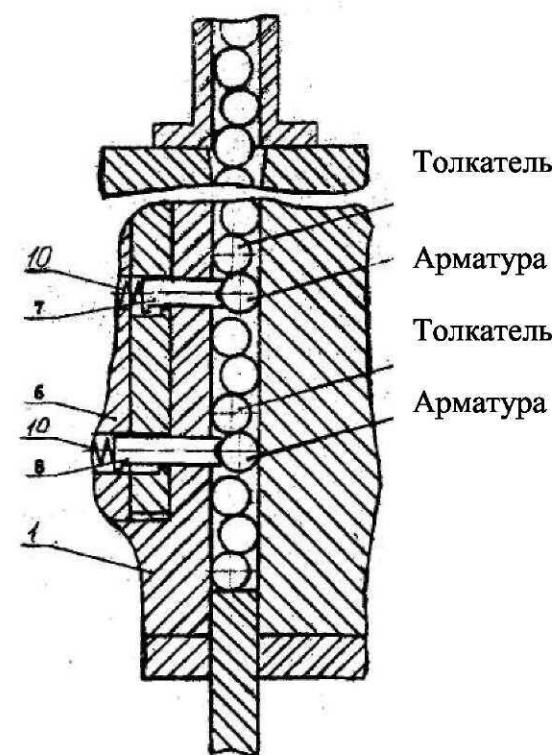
Пресс-форма для изготовления детали «гофрированная втулка»:
